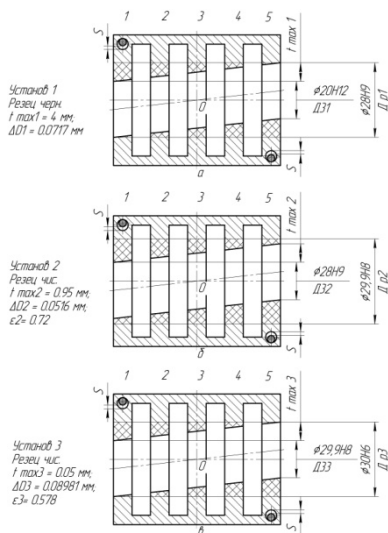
Схемы расположения припусков в заготовке по отношению к оси борштанги пиноли при смене резцов: а – чернового; б – получистового; в – чистового
